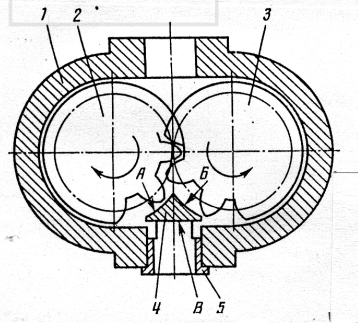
Схема шестеренного гідромотора з пристроєм для покращення пуску: 1- корпус; 2,3- шестерні зовнішнього зачеплення; 4- пристрій для покращення пуску; 5- втулка
